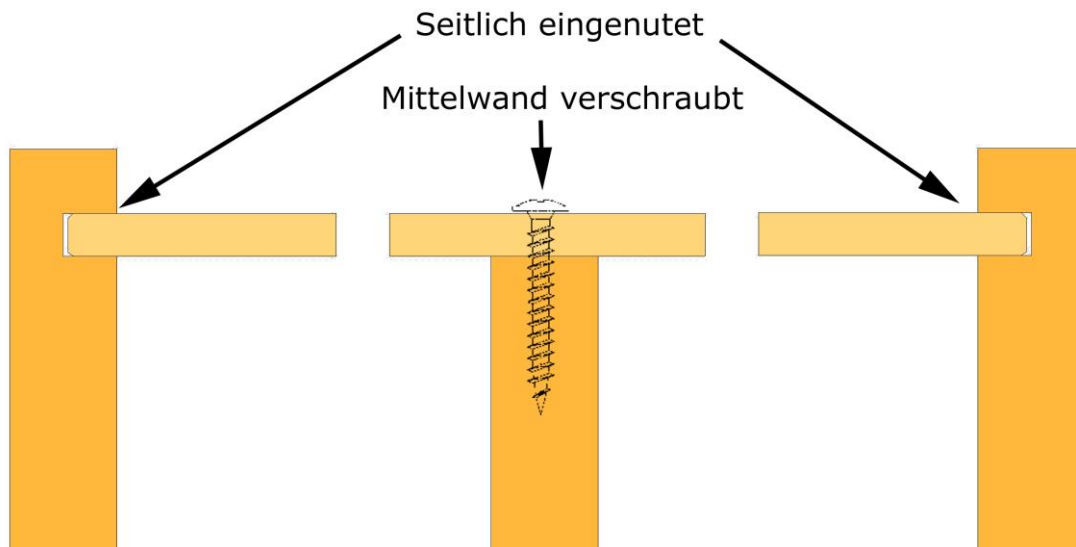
Konstruktion einer Mittelwand/ Rückwand
